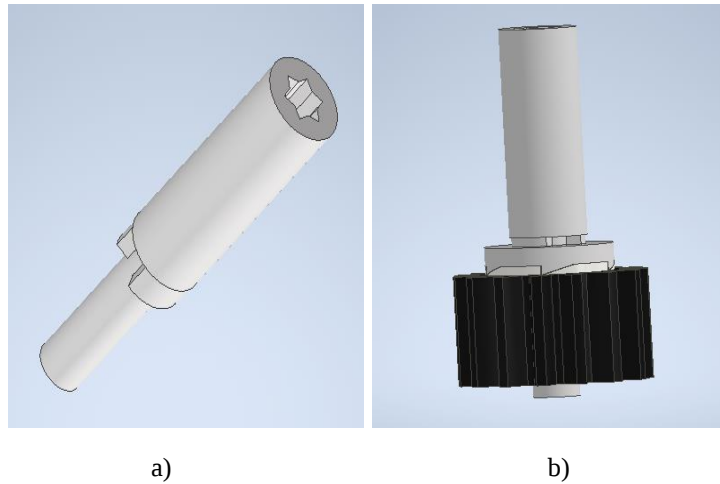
a) Tubo b) Planeta con sistema de trinquetes
